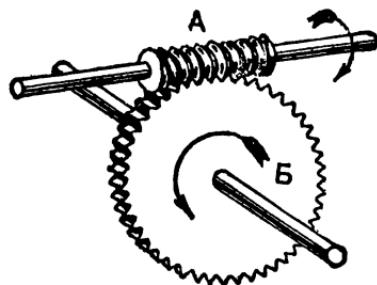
Схема червячного редуктора: А — червяк; Б — шестерня.
